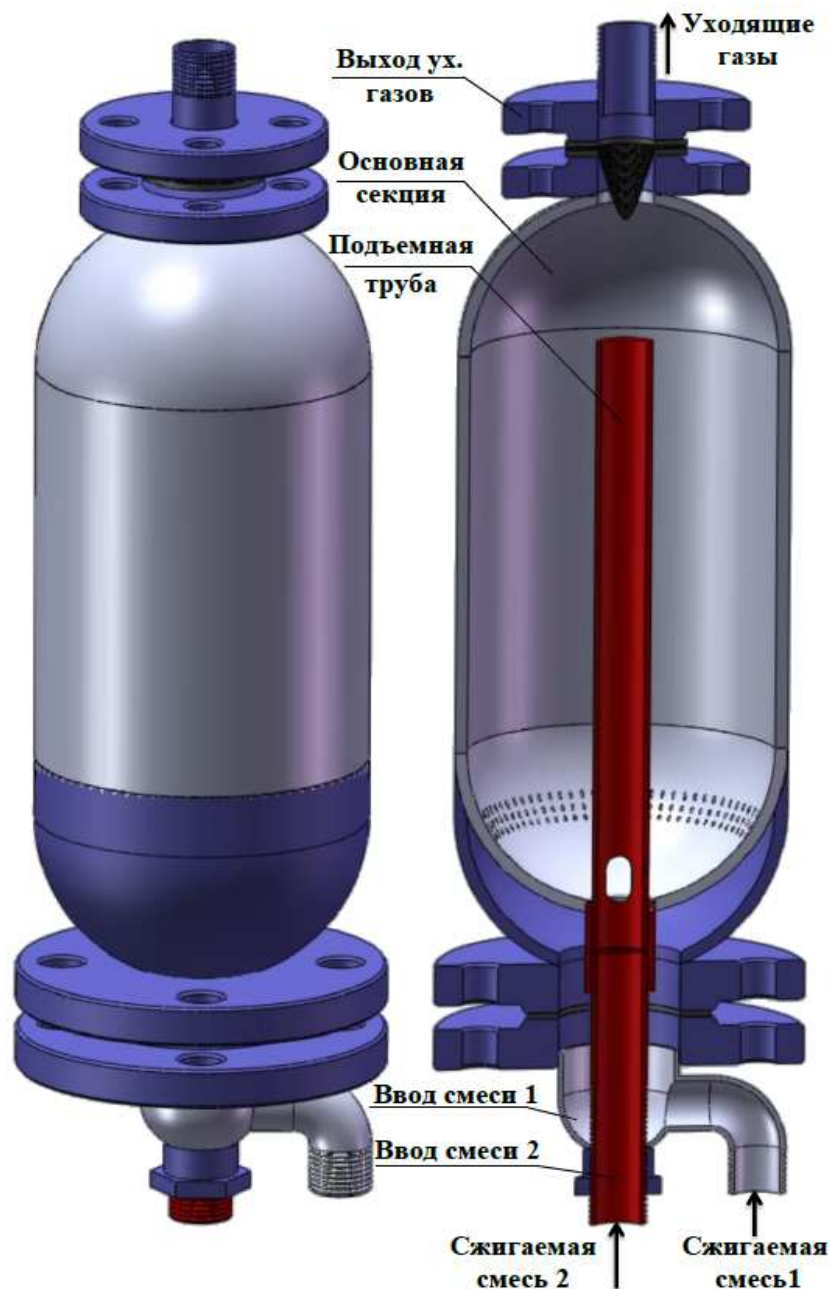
Конструктивное исполнение каталитического устройства сжигания с сонаправленным и противоположным движением наполнителя и сжигаемой смеси
